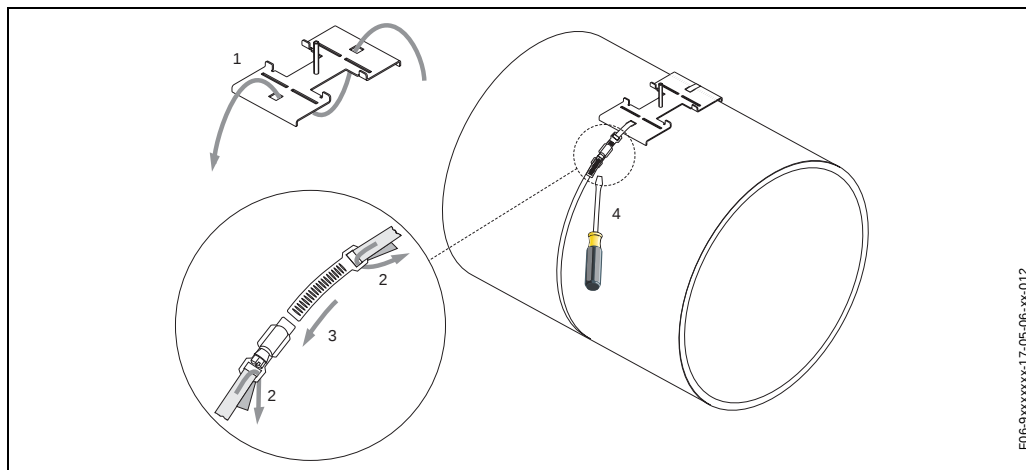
Установка натяжного обруча для трубы ДУ 250...4000
